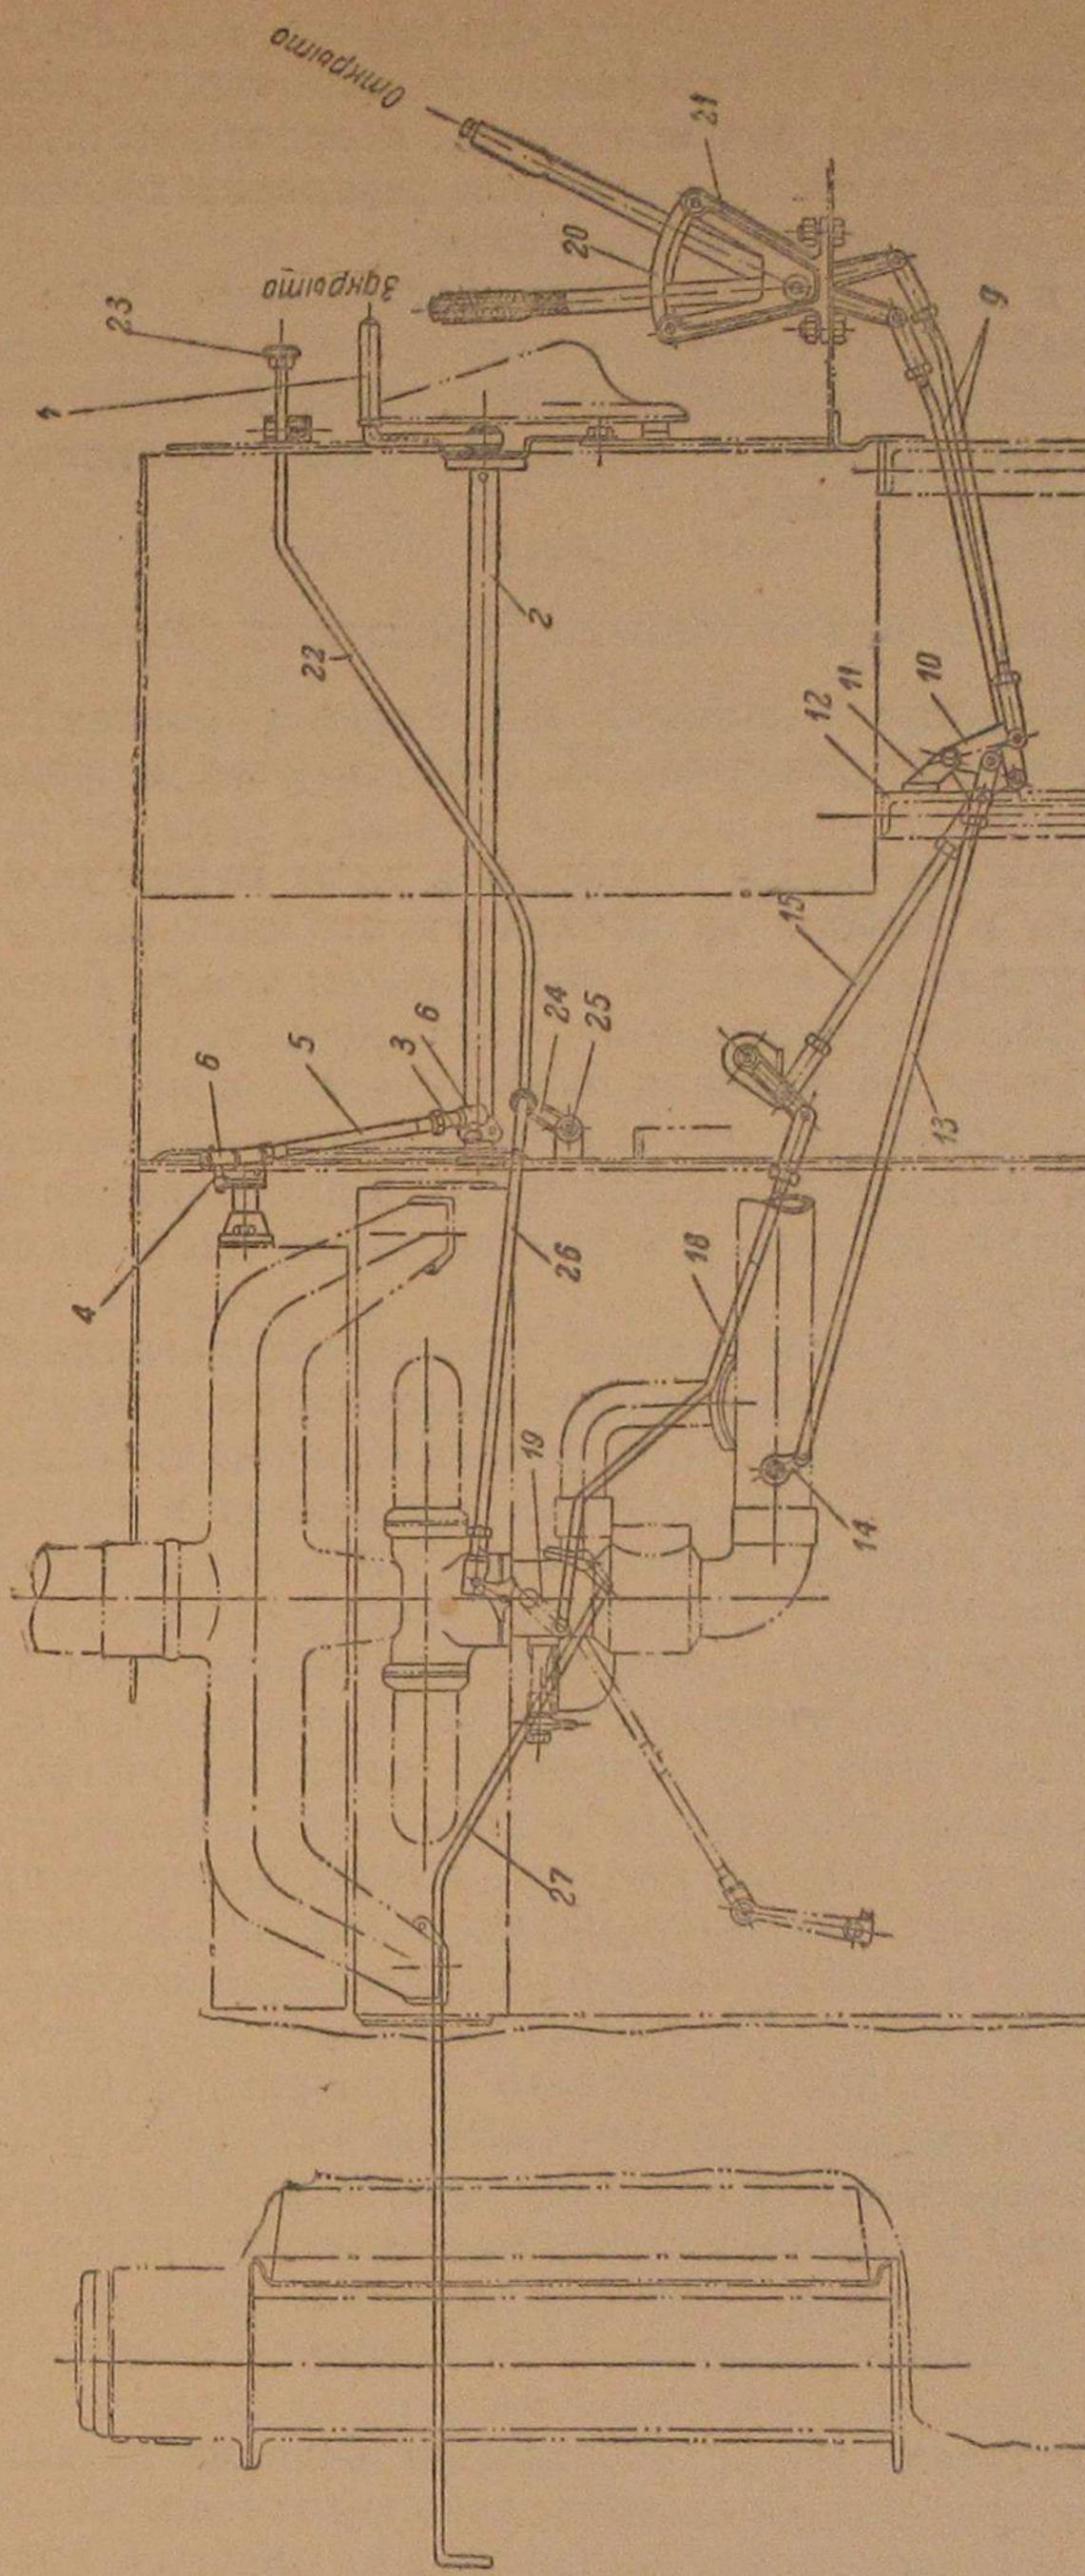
Тяги и рычаги механизма управления двигателем (вид сбоку) (Подпись под рисунком — см. рис. 33).
